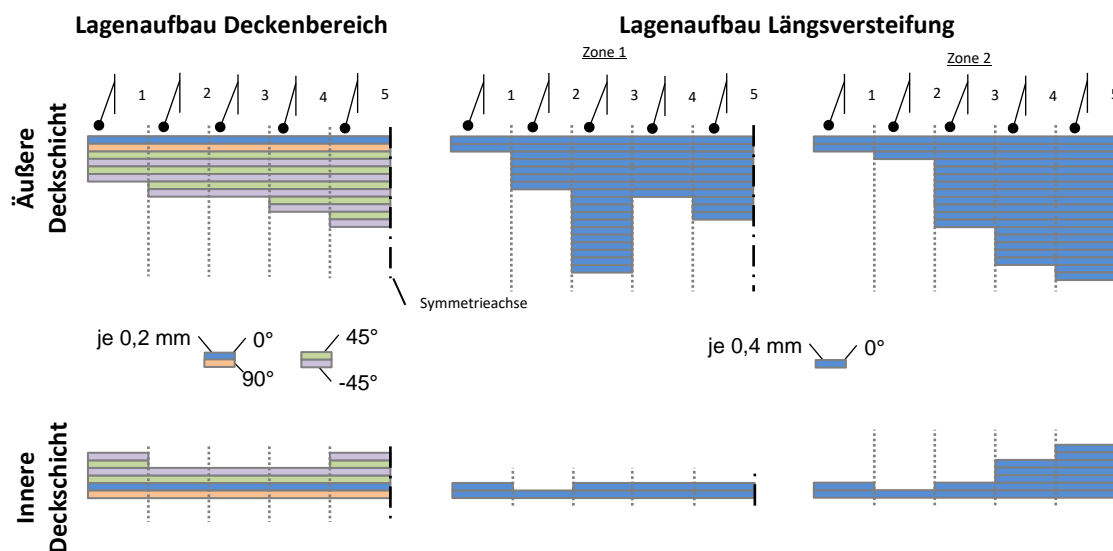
Laminatdicken für die Segmente 1 bis 5 am Beispiel des VARI-Verfahrens für äußere und innere Deckschicht des Sandwichaufbaus und der dazugehörigen Längsversteifungen. Links: der Lagenaufbau des Deckenbereichs; Mitte: der Lagenaufbau für die Zone 1 der Längsversteifung; Rechts: der Lagenaufbau für die Zone 2 der Längsversteifung
